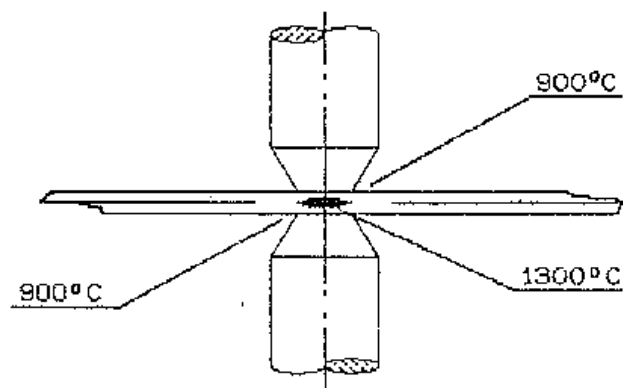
DISTRIBUIÇÃO DO AQUECIMENTO
